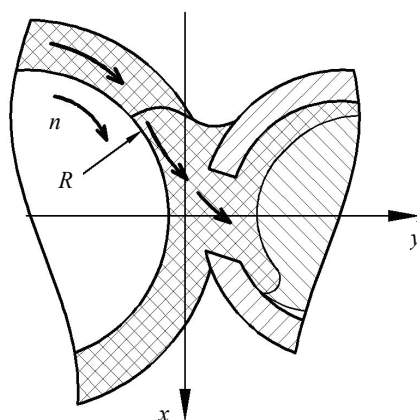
Схема движения материала с поверхности валка в загрузочное отверстие винтового канала шнека
